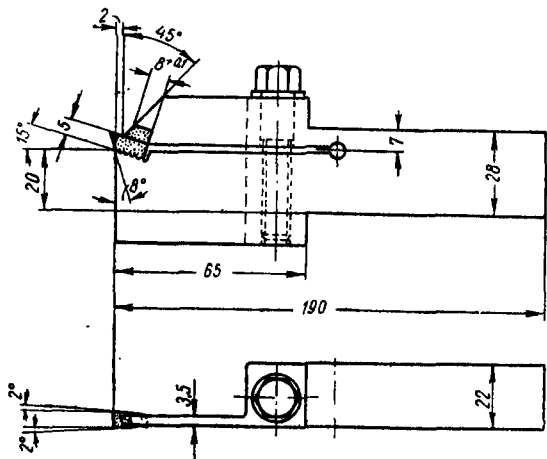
Отрезной резец с механическим креплением твердосплавной пластинки.
